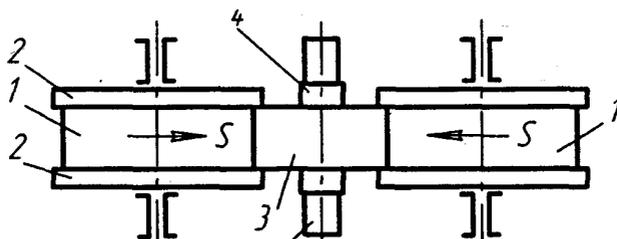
Пример изготовления зубчатого колеса накатыванием:
